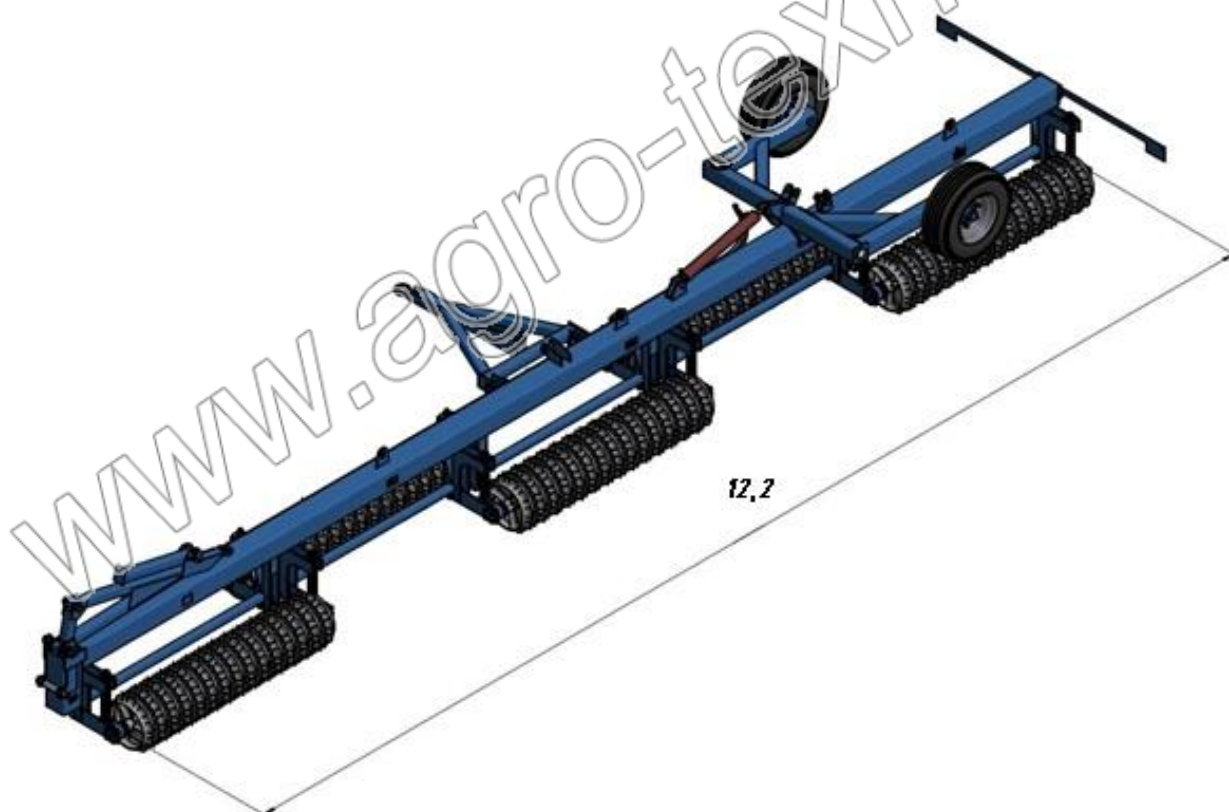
а Габаритные размеры в рабочем положении КЗК-12У.
